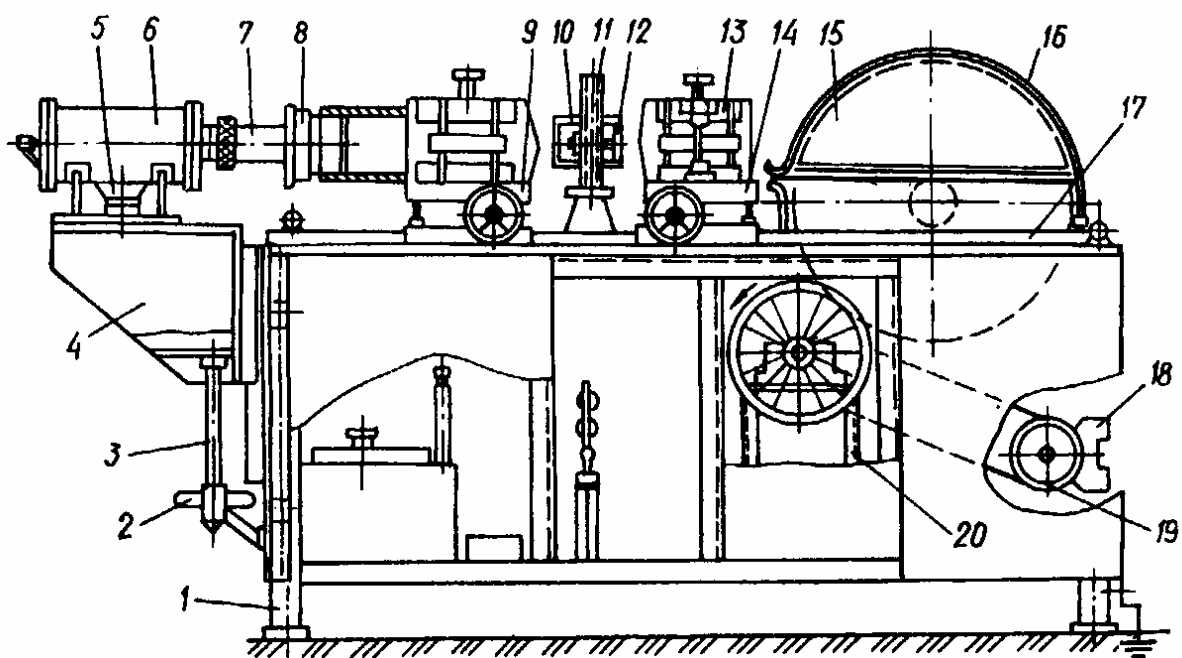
Універсальний верстат для обробки й зварювання пластмасових труб:
